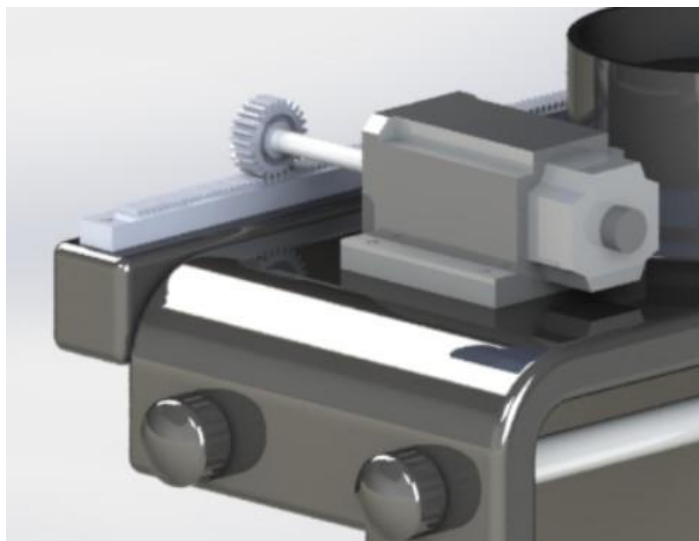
Vista detall engranatges de la mà robòtica [Font: Pròpia]
